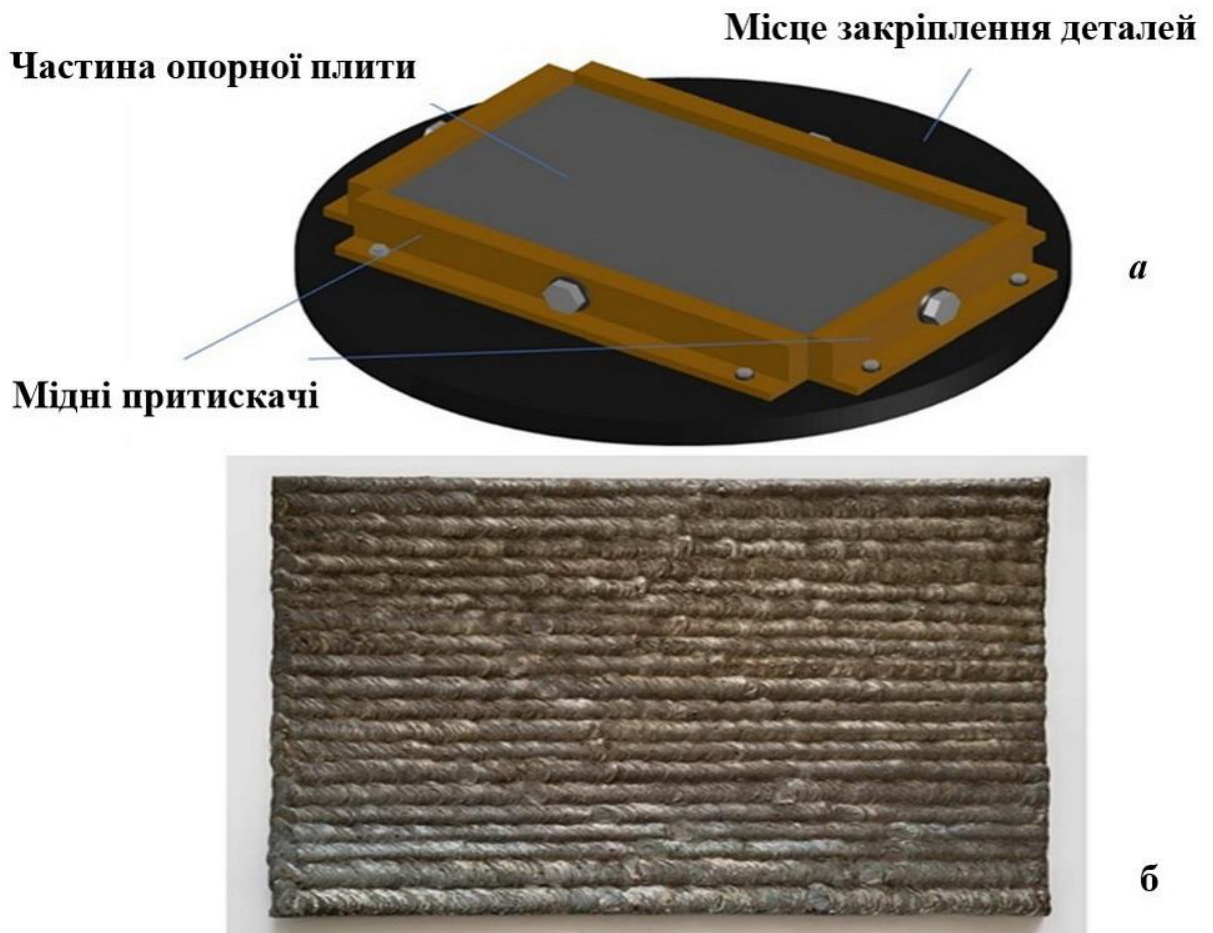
а – Загальна схема закріплення частини опорної плити для наплавлення із запобіганням розтікання рідкого металу з використанням мідних притискачів, б – загальний вигляд опорної плити після наплавлення та зварювання
